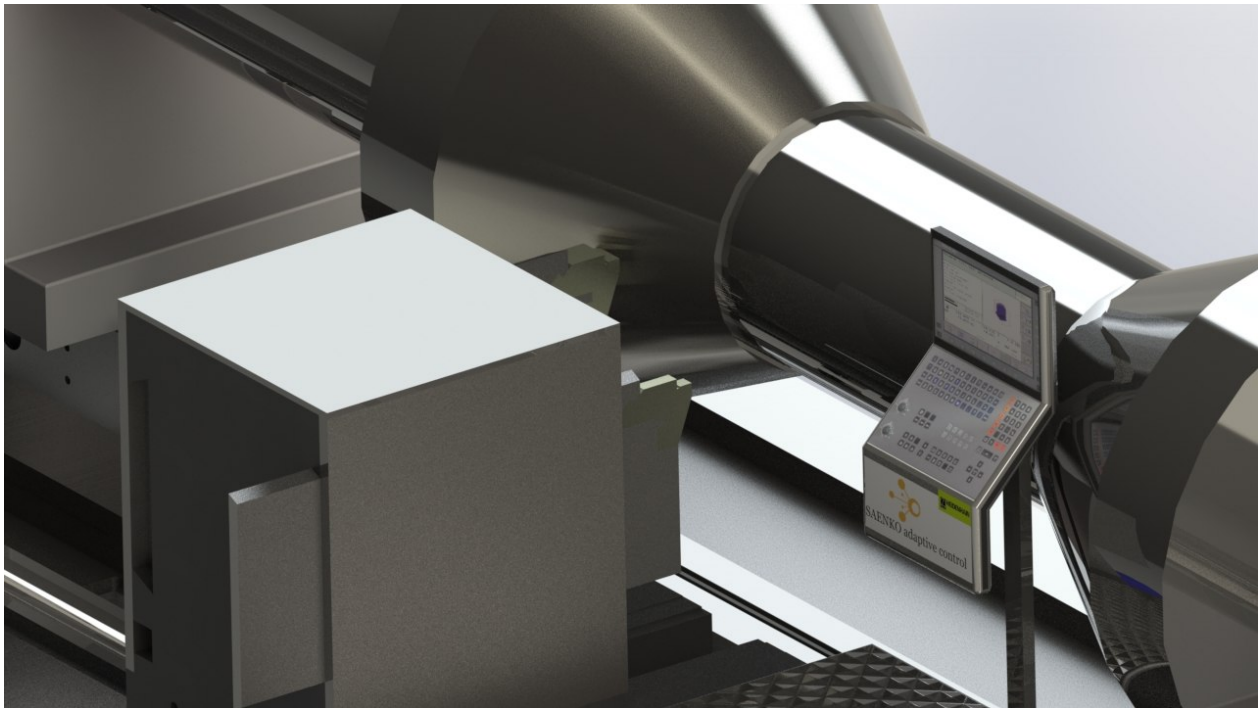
Тривимірний модель обробки деталі на важкому токарному верстаті з ЧПК
